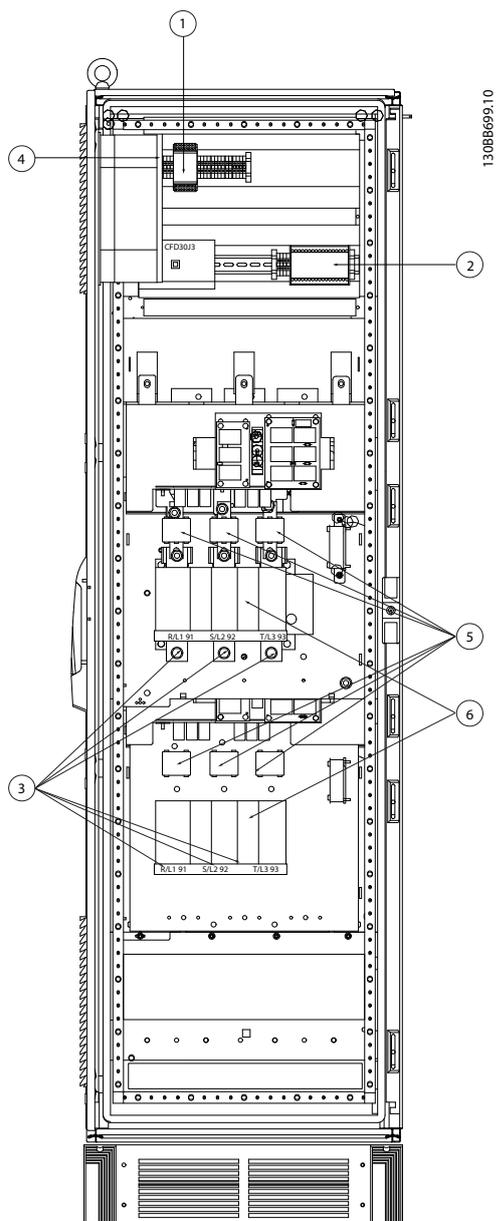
Шкаф инвертора, типоразмер F14
